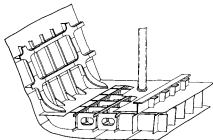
Крестообразный сварной лист соединяет плосков бортового стрингера и рамного шпангоута.
